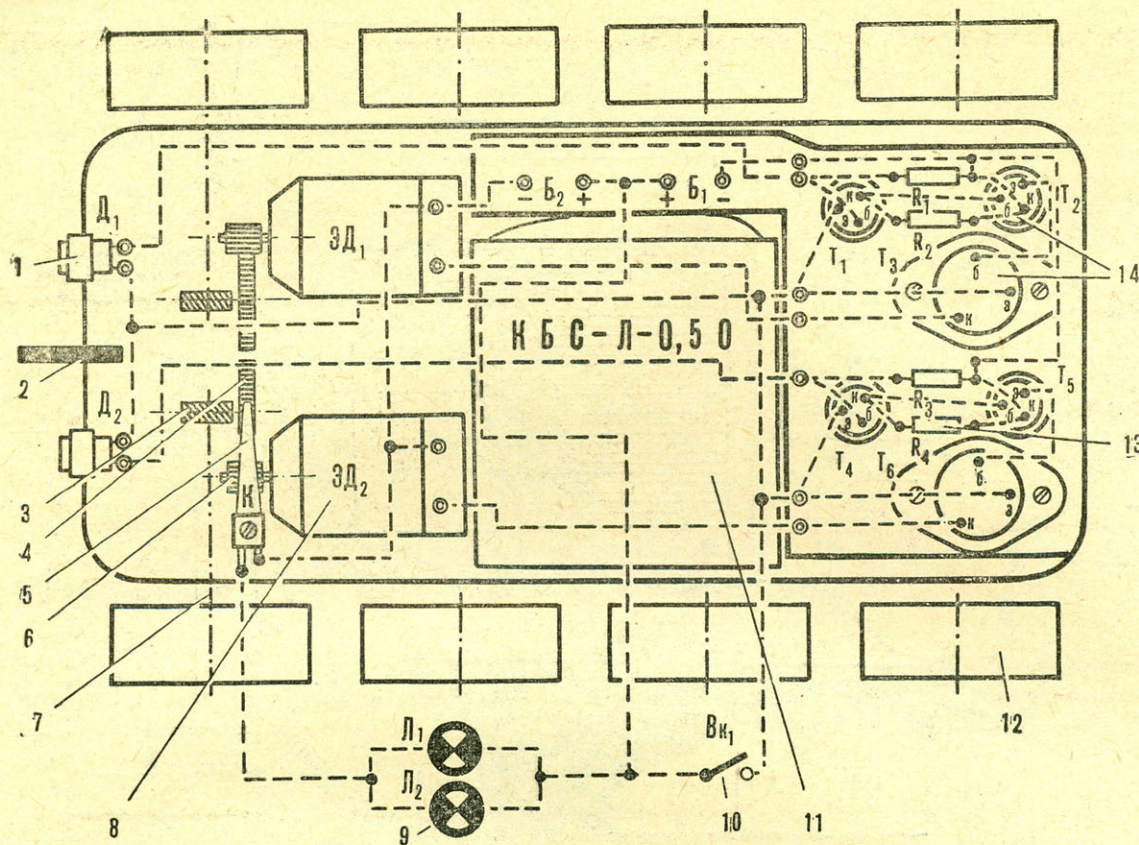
Расположение электрических и механических узлов шасси модели «Лунохода-1»: 1 — фотоэлемент; 2 — светонепроницаемая пластина; 3 — червяк, соединенный с шестерней полуоси; 4 — шестерня редуктора; 5 — прерыватель работы фар; 6 — шестерня вала двигателя; 7 — ведущая полуось; 8 — электродвигатель; 9 — лампочки фар; 10 — тумблер; 11 — батарея; 12 — колесо; 13 — сопротивление; 14 — транзисторы.
